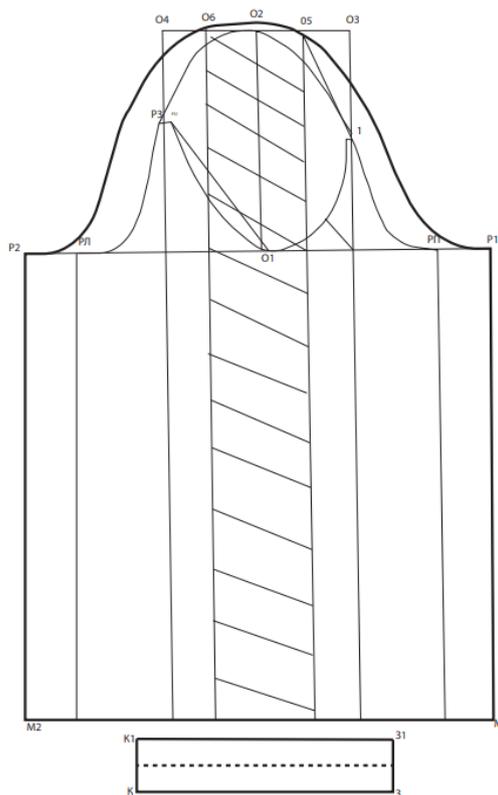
Чертеж модельной конструкции рукава для женского платья
